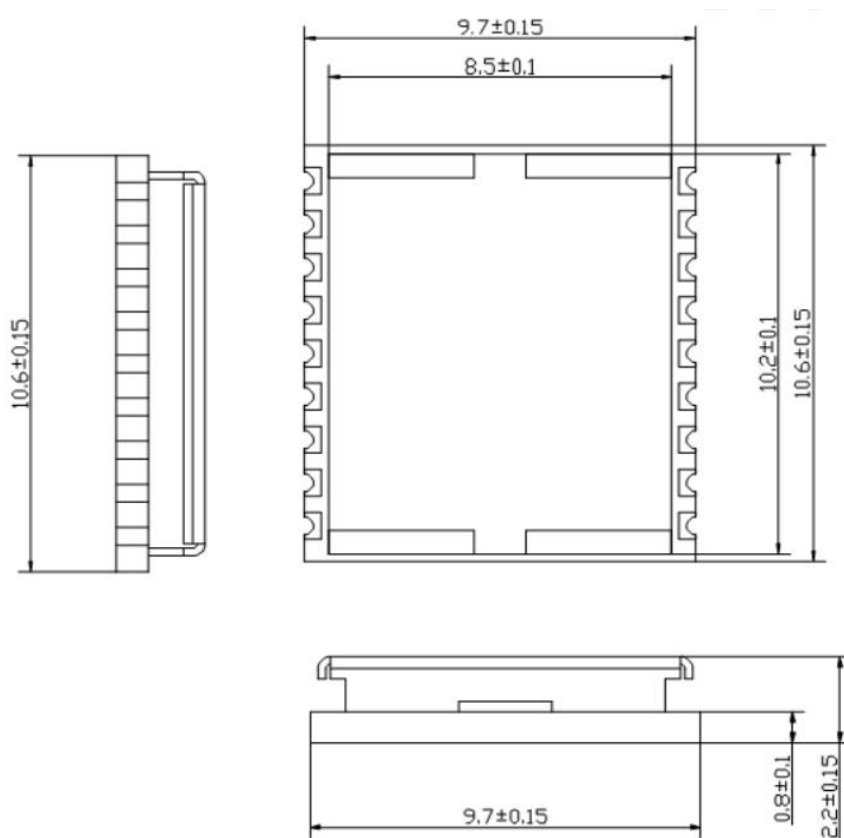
WT0601 俯视和侧视尺寸 (单位:mm)
